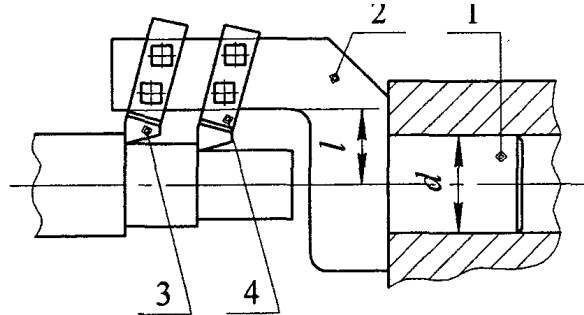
Державка для обточування зовнішніх поверхонь, що встановлюється в гнізді револьверної головки: 1 - хвостовик; 2 - тіло державки; 3 і 4 - різці
